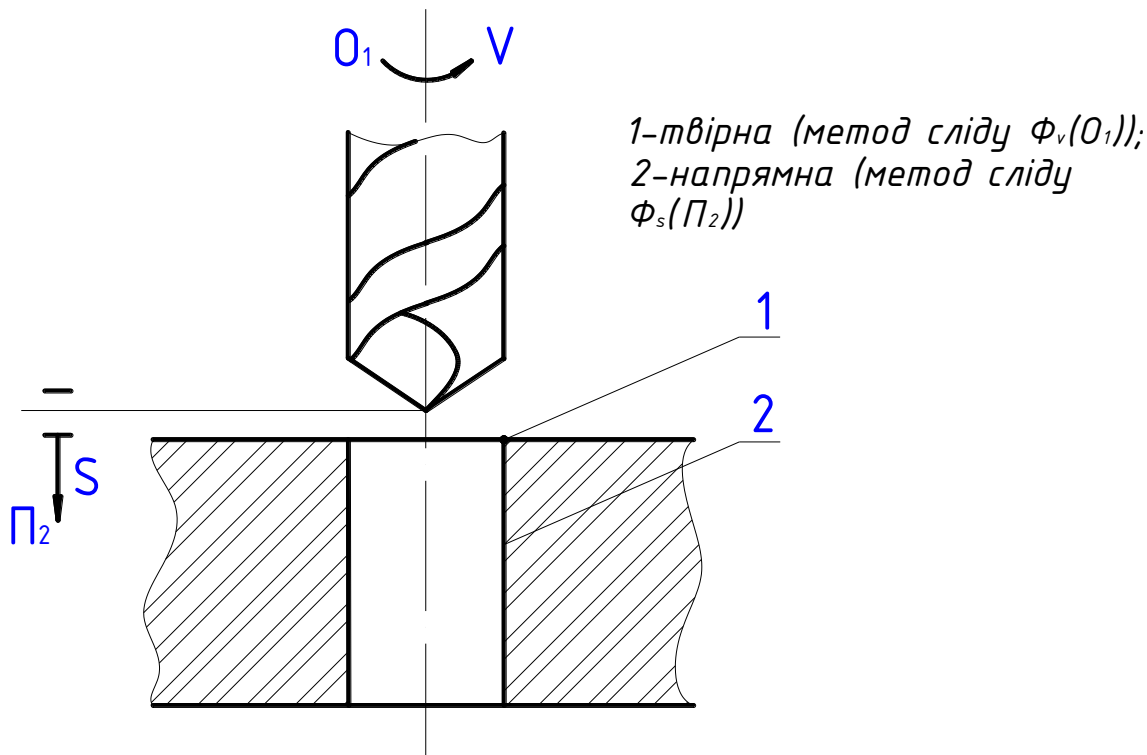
Рух інструменту при свердлінні отвору.
